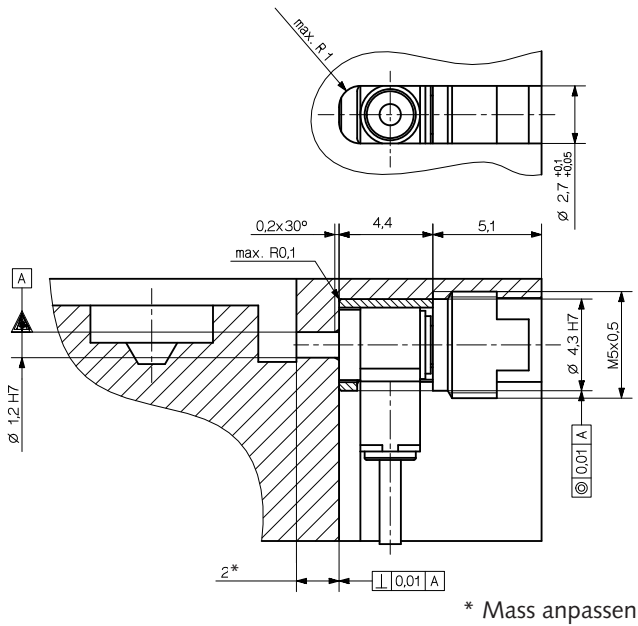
Einbau mit Distanzhülse Typ 6466 und Montagenippel Typ 6465
